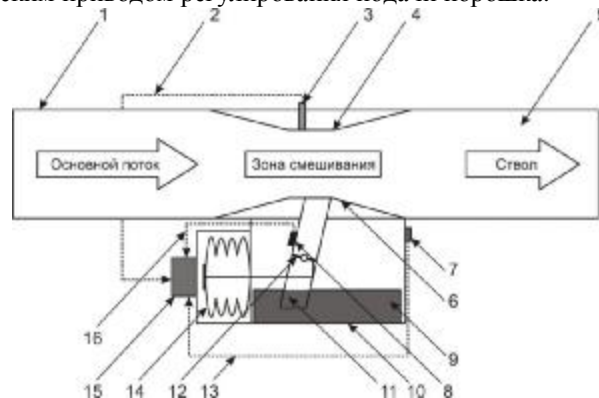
Схема эжекторного смесителя «воздух-порошковая смесь» с пневматическим приводом регулирования подачи порошка:
